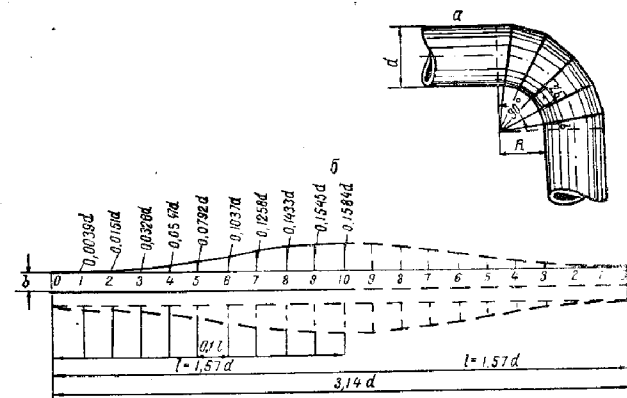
Сварной отвод 90°, состоящий из четырех звеньев и двух стаканов.
